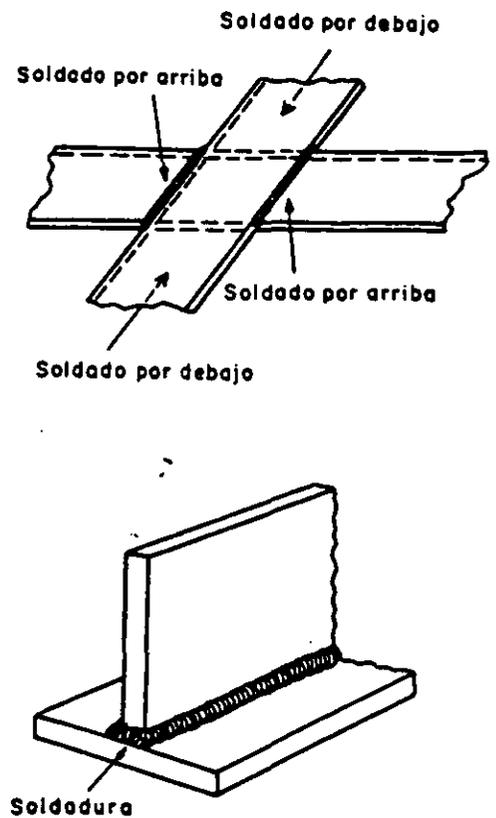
Las superficies solapadas deben cerrarse completamente a lo largo de todo su contorno mediante un cordón de soldadura continuo.
